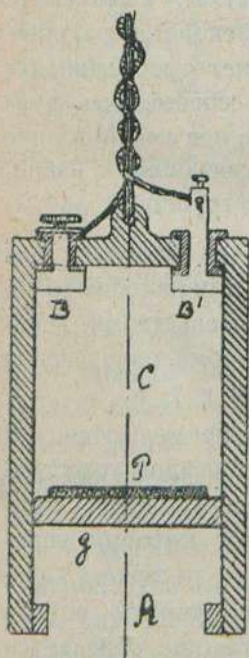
Поплавок посадочного приспособления гидроаэроплана.
